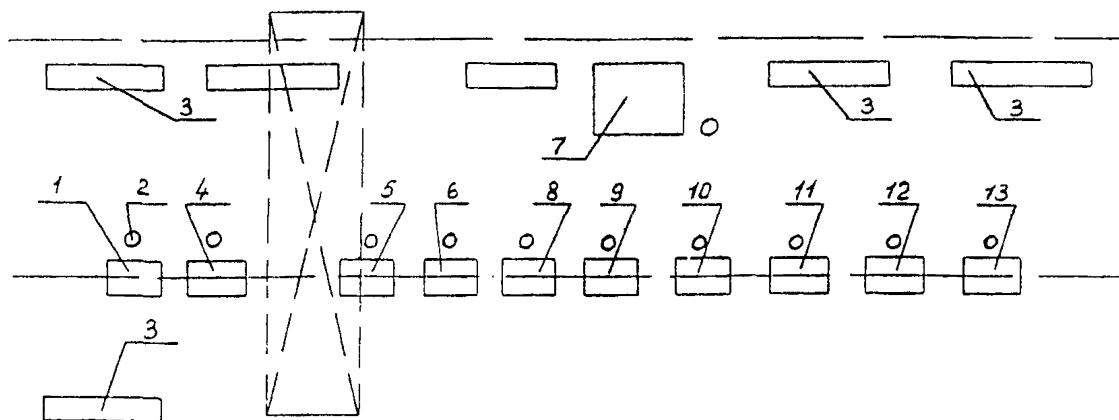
Типовая схема планировки рабочего места общей сборки автомобиля
